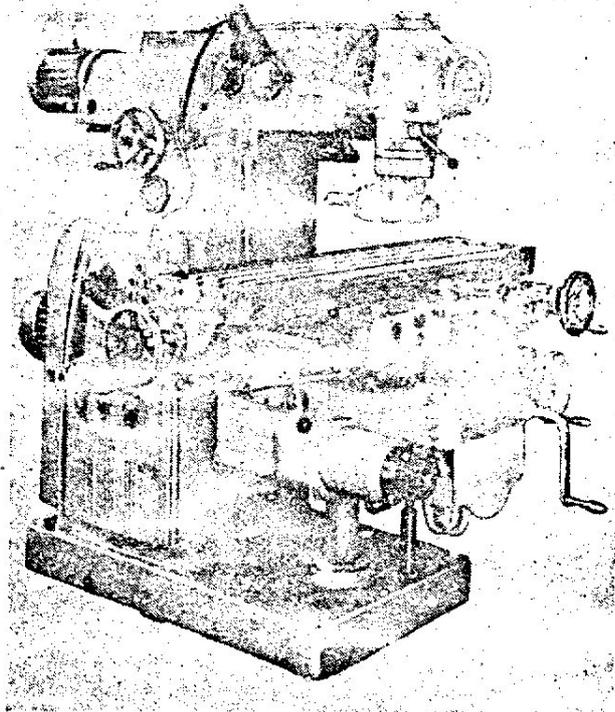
Широкоуниверсальный консольно-фрезерный станок модели 6М82Ш
